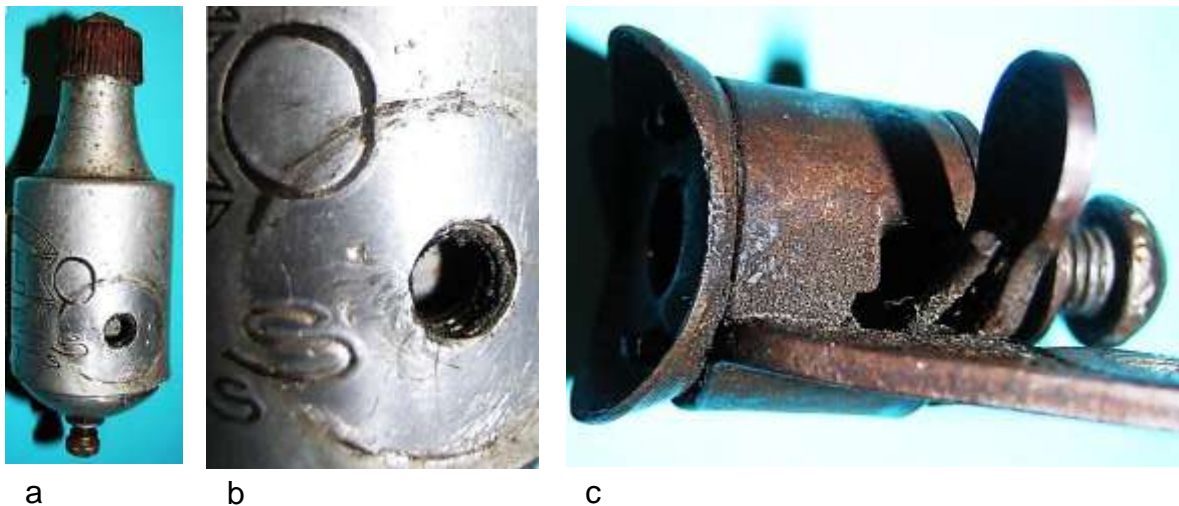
Befestigung der Kippvorrichtung: a) Sitz am Gehäuse, b) Gewindebohrung hinter der Gehäusewand, c) Kippvorrichtung mit dem Flansch und dem als Schraube ausgeführten Drehbolzen.
